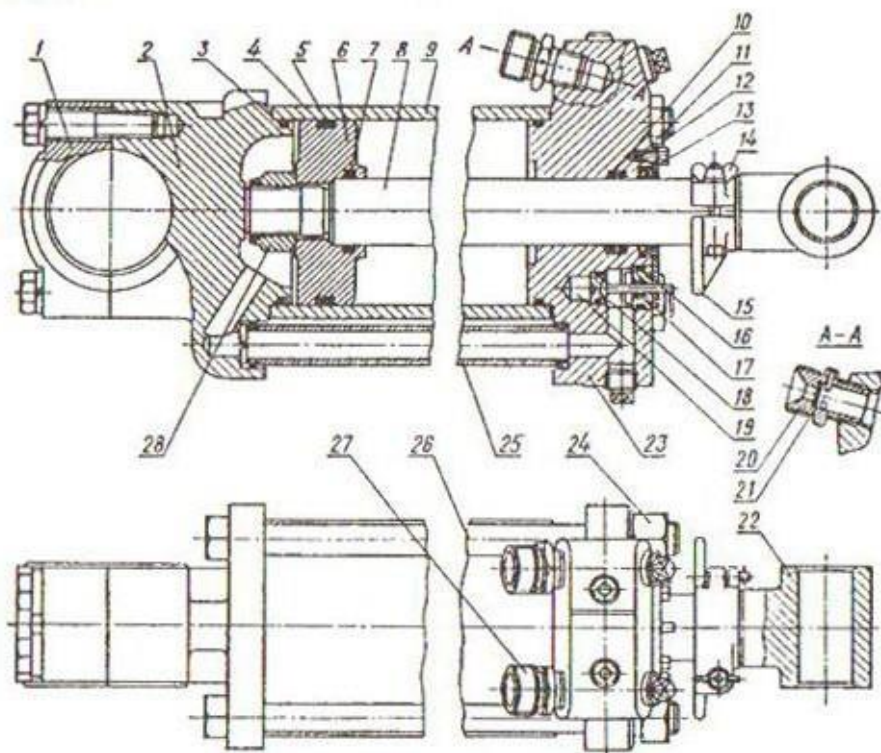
Гидроцилиндр: 1 - бугель; 2 - задняя крышка; 3,5,7,10,16 – уплотнительные резиновые кольца; 4 - кольцо; 6 – поршень; 8 - шток; 9 - цилиндр; 11 - болт; 12 – шайба; 13 – «чистик»; 14 – барашковая гайка; 15 – упор; 17-направляющая клапана; 18 – гидромеханический клапан; 19 – гнездо клапана; 20 – штуцер замедлительного клапана; 21 – шайба замедлительного клапана; 23 – передняя крышка, 24 – гайка; 25 – соединительная трубка; 26 – болт; 27 – штуцер; 28 – гайка штока.
